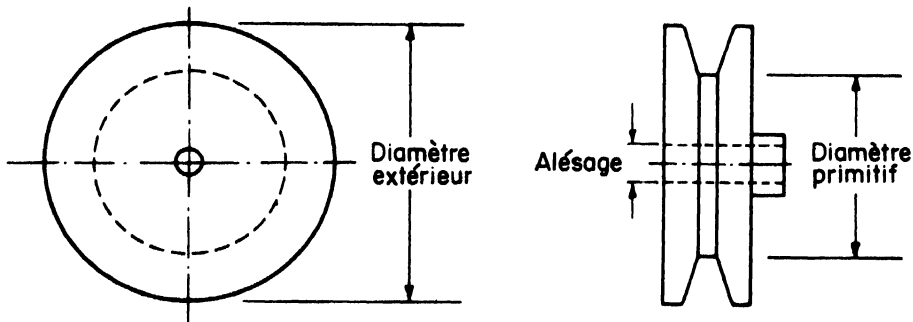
DETAILS DE CONSTRUCTION DE POULIE POUR COURROIE TRAPEZOIDALE
